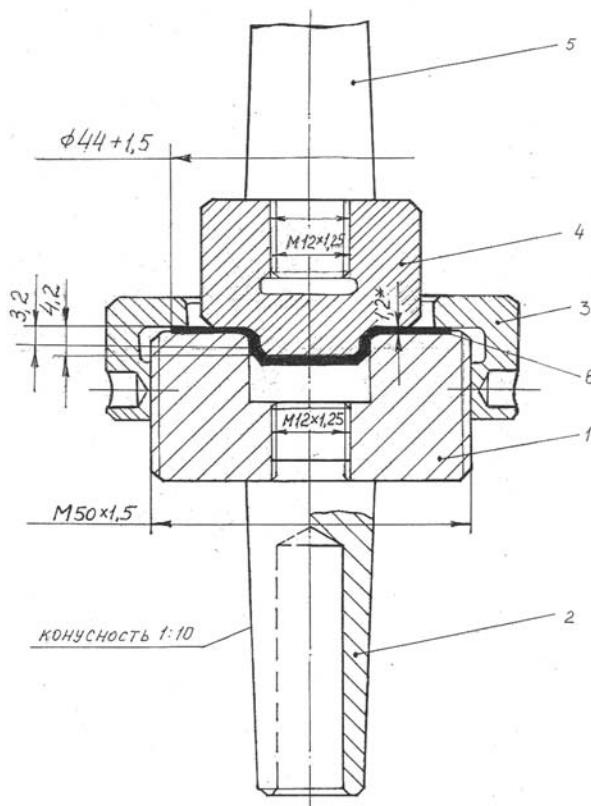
Схема устройства для деформирования листовых заготовок из титановых сплавов при нагреве:
